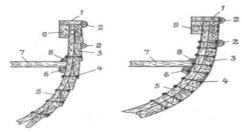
Обшивка: а — внакрой; б — вгладь; 1 — планширь; 2 — буртики; 3 — доски обшивки; 4 — гвозди с шайбами; 5 — шпангоут; 6 — подлегарс; 7 — банка; 8 — штапик; 9 — привальный брус
